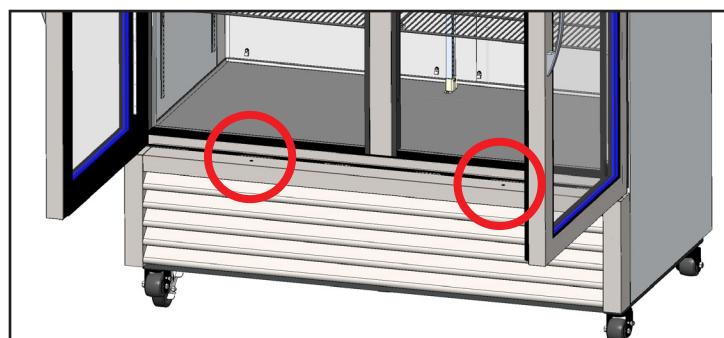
Винты крепления жалюзийной решетки под распашными дверцами
